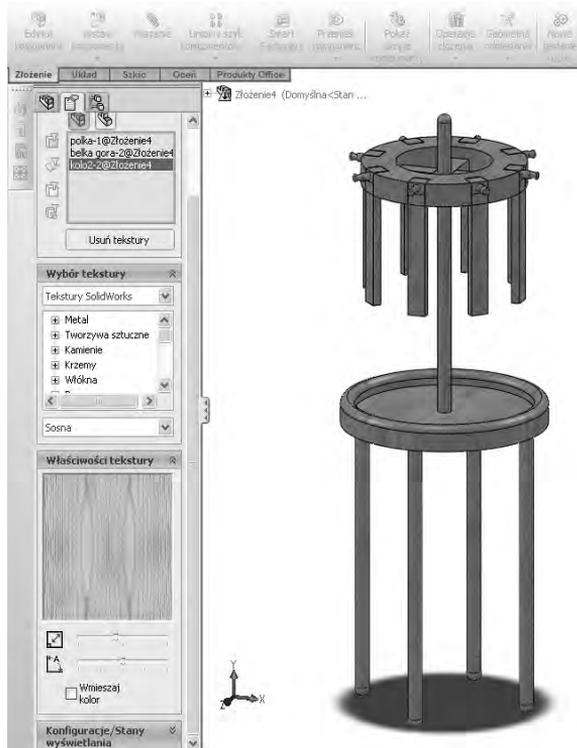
Widok zaimportowanych obiektów do przestrzeni złożeń
